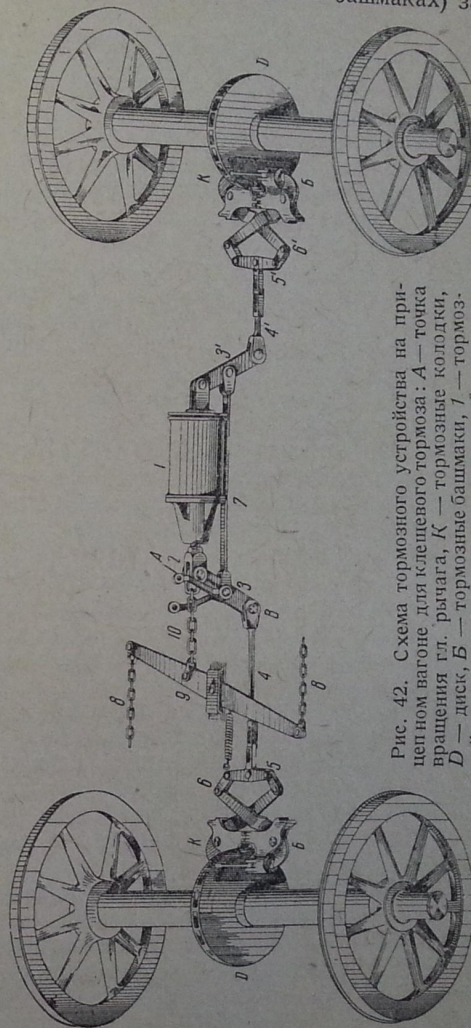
Схема тормозного устройства на прицепном вагоне для клещевого тормоза: *А* — точка вращения гл. рычага, *К* — тормозные колодки, *Д* — диск, *Б* — тормозные башмаки, 1 — тормозной цилиндр, 2 — шток тормозного цилиндра, 3 и 3' — главные рычаги, 4 и 4' — тяги к клещам, 5 — траверза, 6 — клещи (система рычажков), 7 — средняя тяга, 8 — цепи ручного тормоза, 9 — рычаг ручного тормоза, 10 — передаточная цепь.
